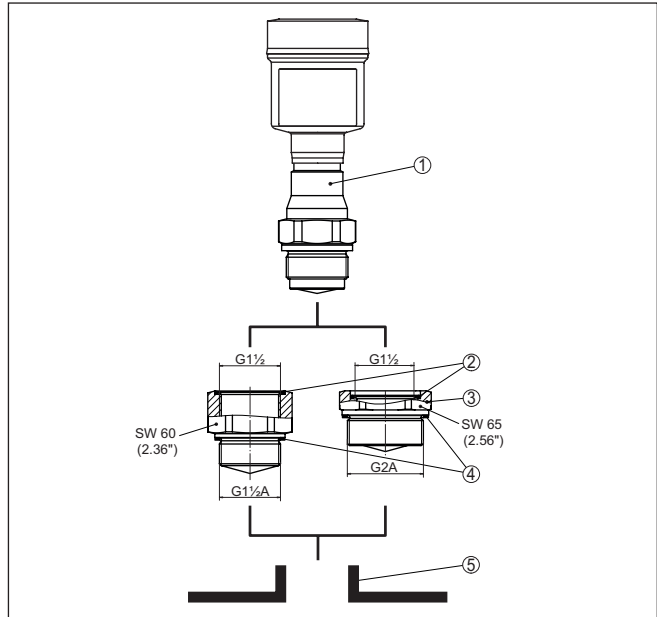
NCR-86 mit PTFE-Gewindeadapter (Beispiel NCR-86 mit Gewinde G1½)
